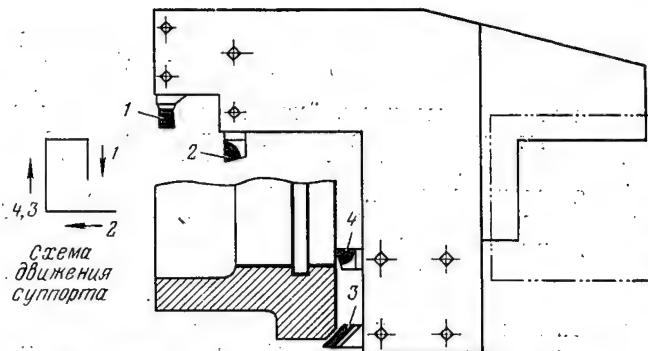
Многорезцовая державка для обработки поверхностей без поворота резцедержателя.
